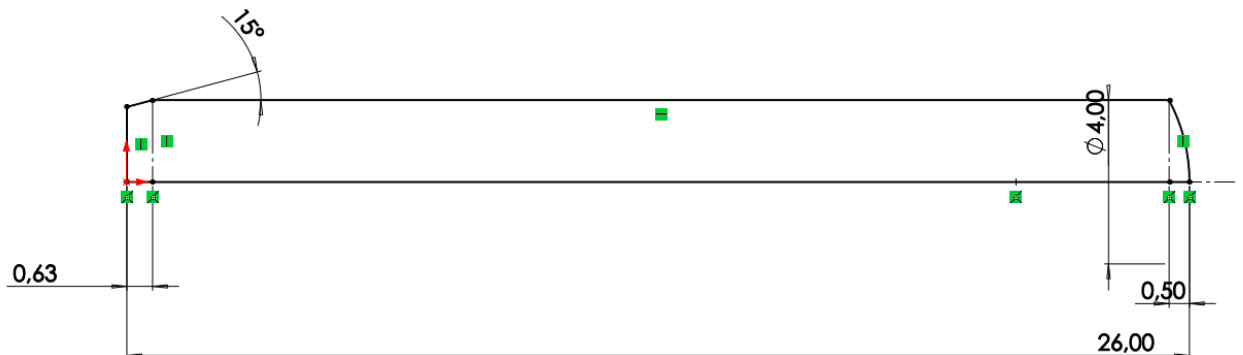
Эскиз детали Штифт - 4ГХ26.
